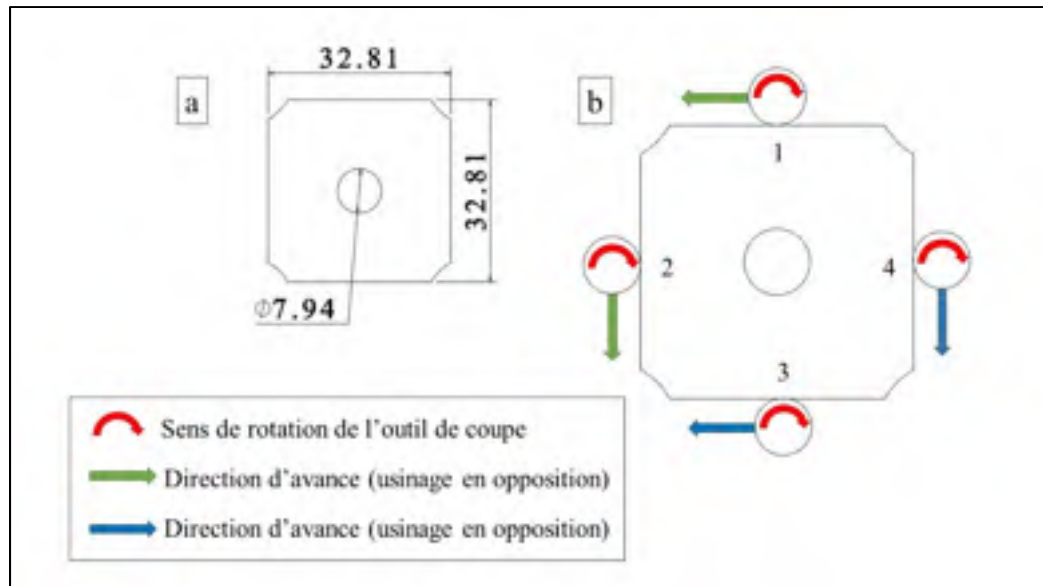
Coupon : a) dimensions et b) modes de coupe sur chaque face
